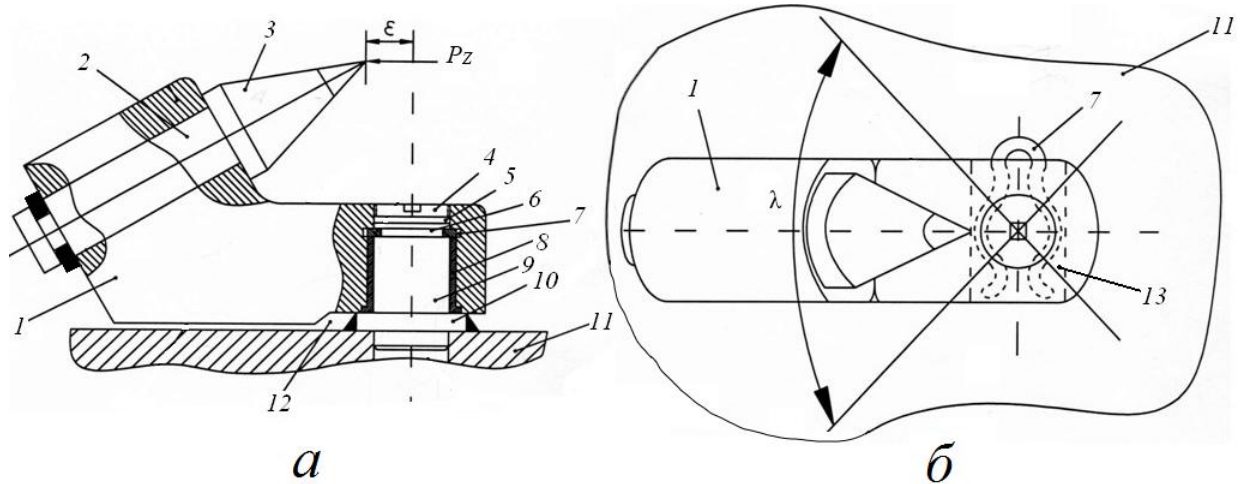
Схема устройства для крепления тангенциального резца на исполнительном органе горного комбайна: а – вид сбоку; б – вид сверху
